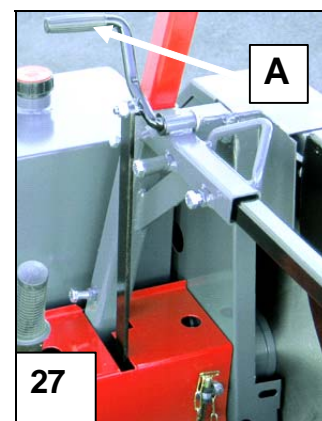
Serrage et desserrage des courroies trapézoïdales
